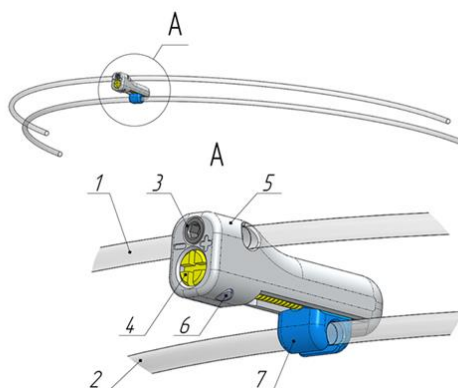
А – регулирующий механизм, 1,2-пластиковые шины, 3-установочный винт, 4-регулирующий винт, 6-штифт, 7-серьга
